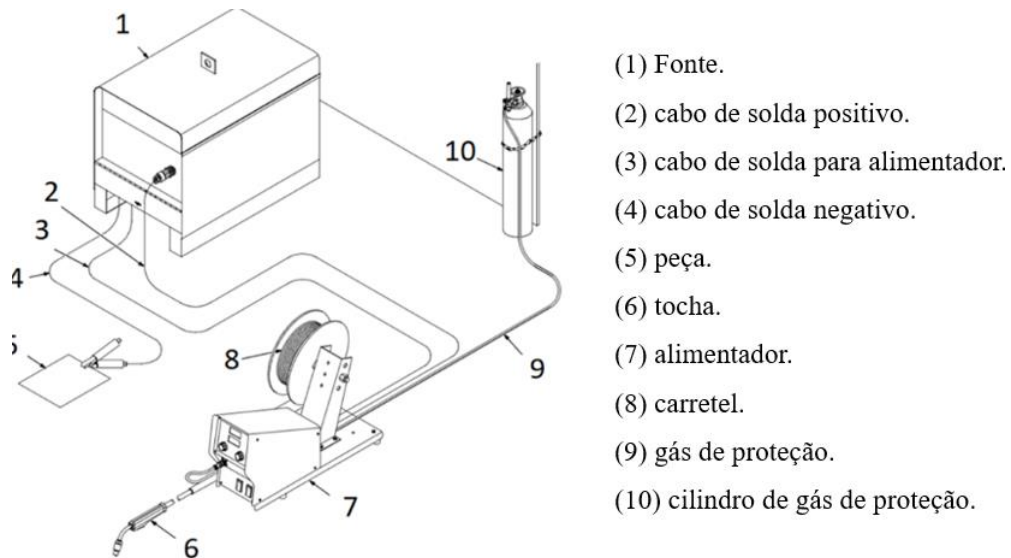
Configuração típica de uma instalação para soldagem MIG.
